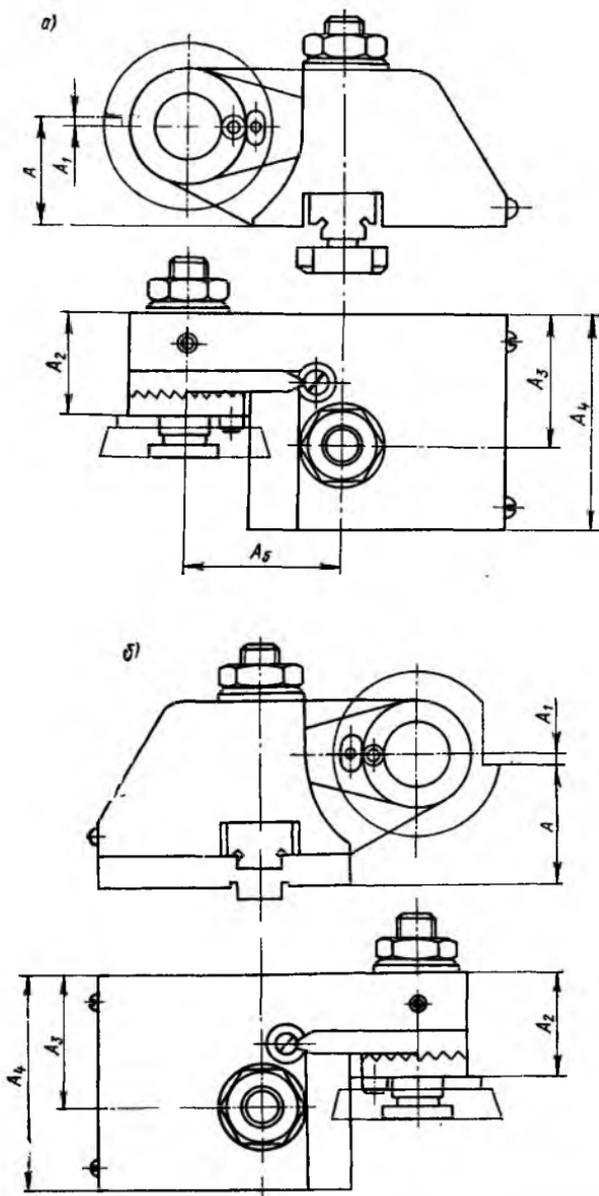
Державки для дисковых фасонных резцов; а — на передний суппорт; б — на задний суппорт
